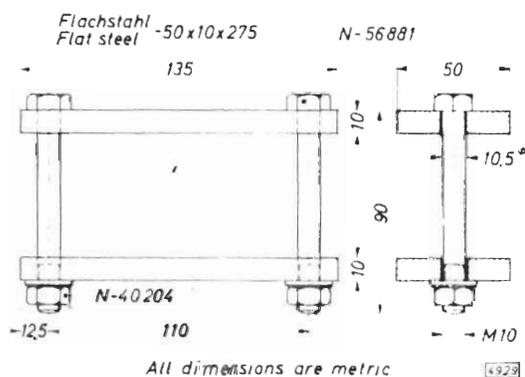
Hilfswerkzeug, bestehend aus 2 Spannplatten, 2 Sechskantschrauben, Muttern, Scheiben
